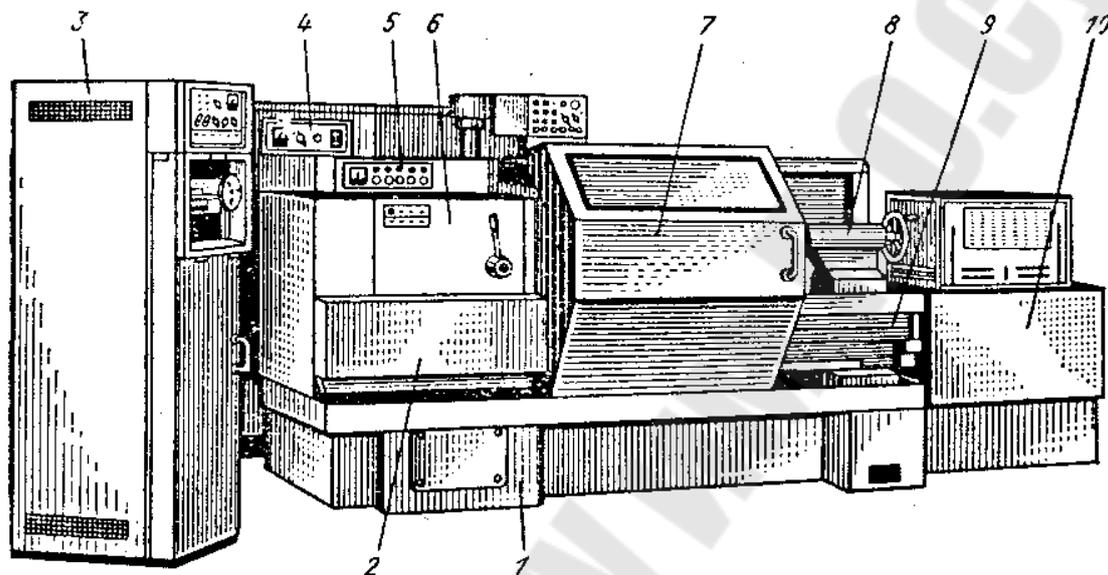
Общий вид токарного станка с ЧПУ
